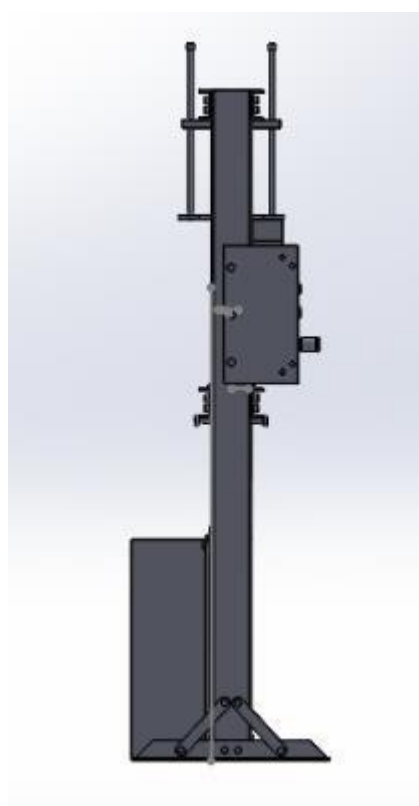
diseño de máquina completa, con todos los accesorios. (vista frontal)
